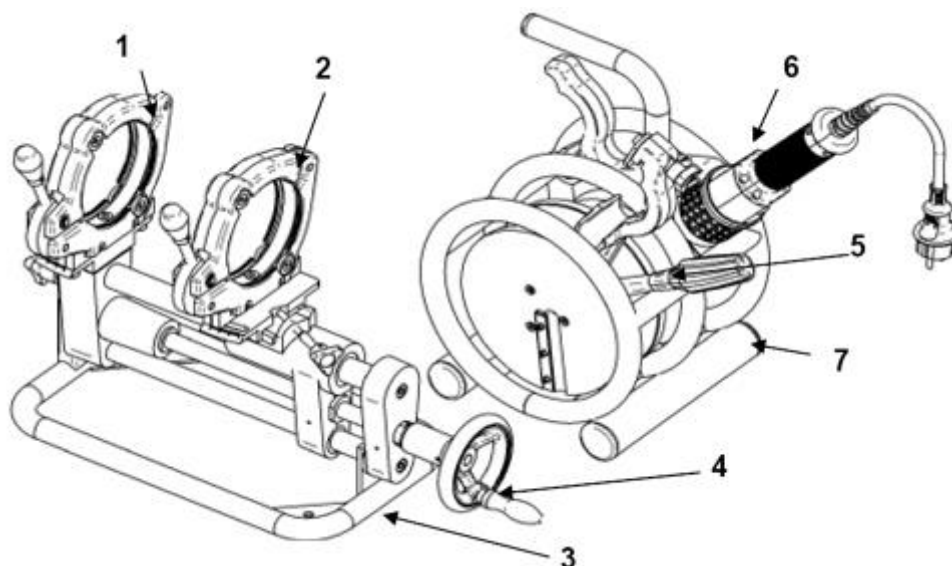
Состав оборудования с механическим приводом для стыковой сварки
